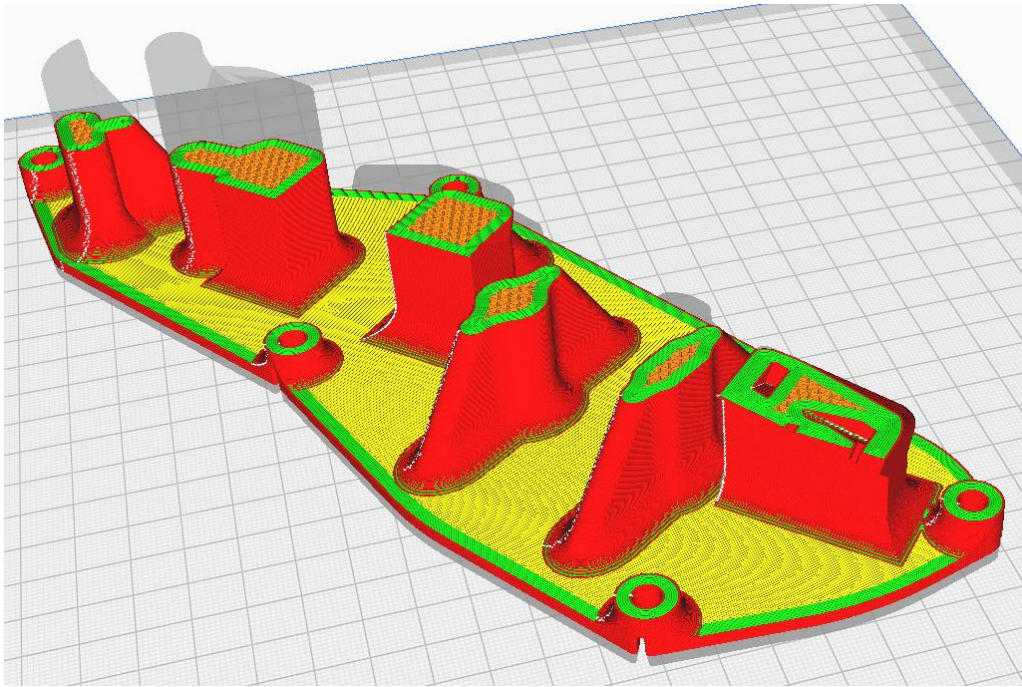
Vista módulo 1 del utillaje para pieza 3 en el laminador de Ultimaker Cura
